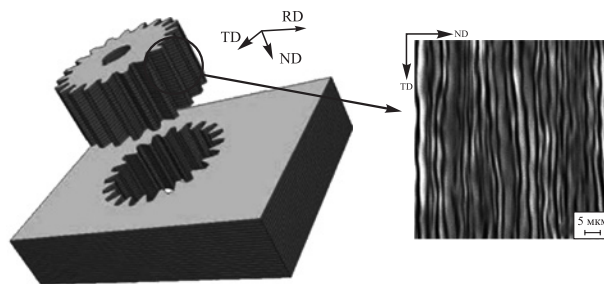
Схема изготовления зубчатого колеса из многослойного материала
